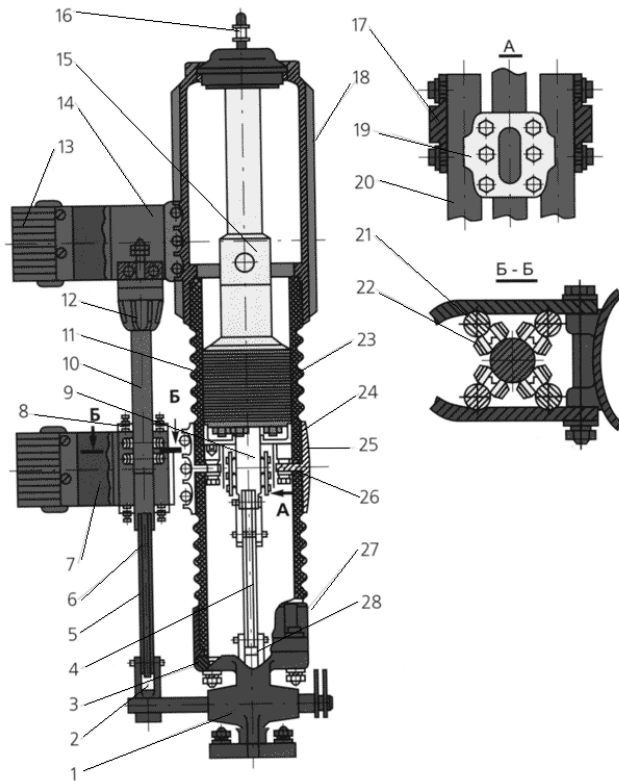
Полюс выключателя ВК-10 на 1600 А: 1 - корпус механизма; 2 - рычаг механизма наружный; 3, 24 - прокладки; 4, 5 - тяги изоляционные; 6, 11 - цилиндры нижний и верхний; 7, 14 - пластины нижняя и верхняя; 8 - токопровод; 9, 10 - стержни подвижные; 12 - контакт неподвижный; 13 - контакт подвижный выдвижного элемента КРУ; 15 - контакт розеточный; 16 - стекло
